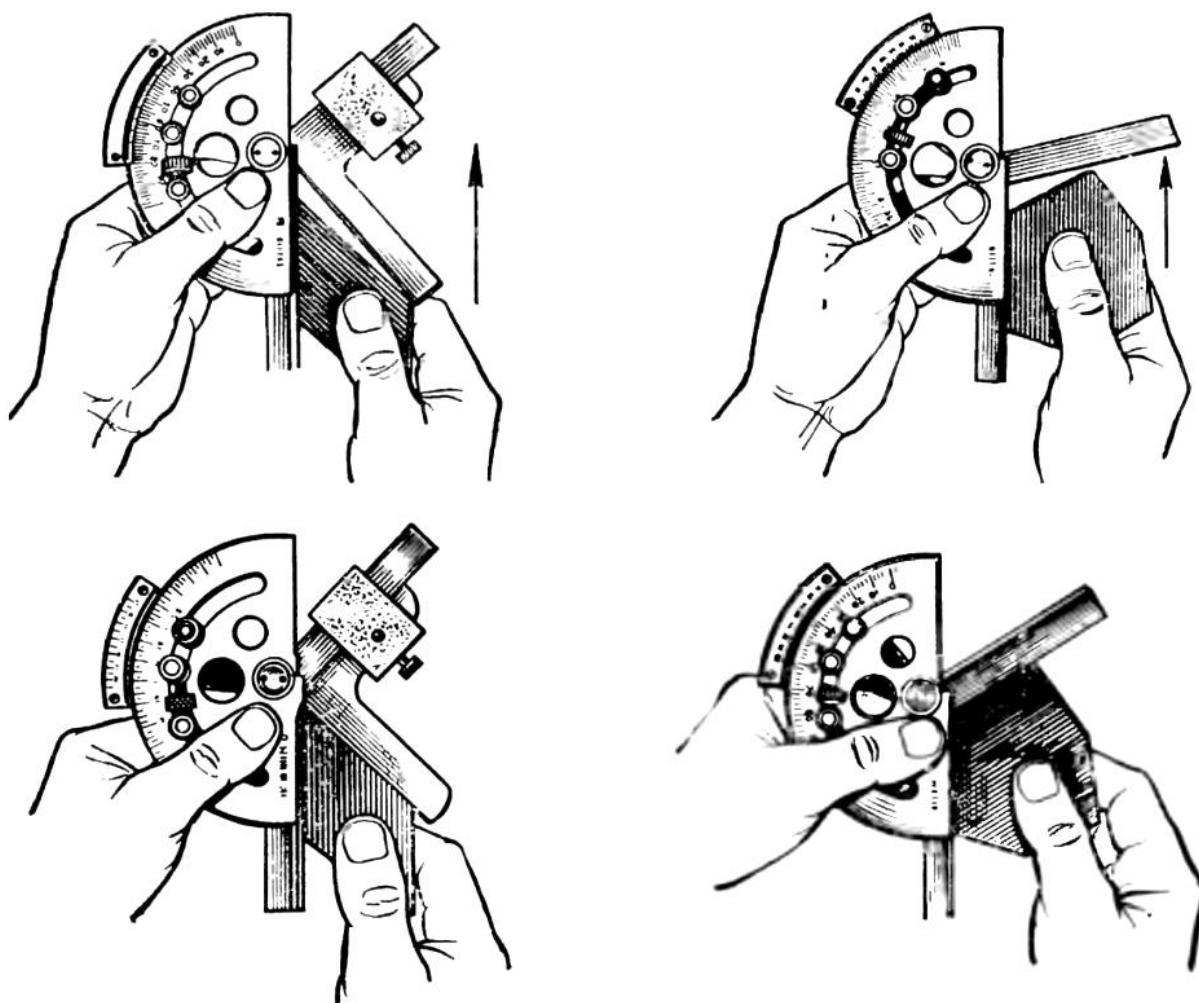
Примеры установки угломера относительно незакрепленной измеряемой детали
